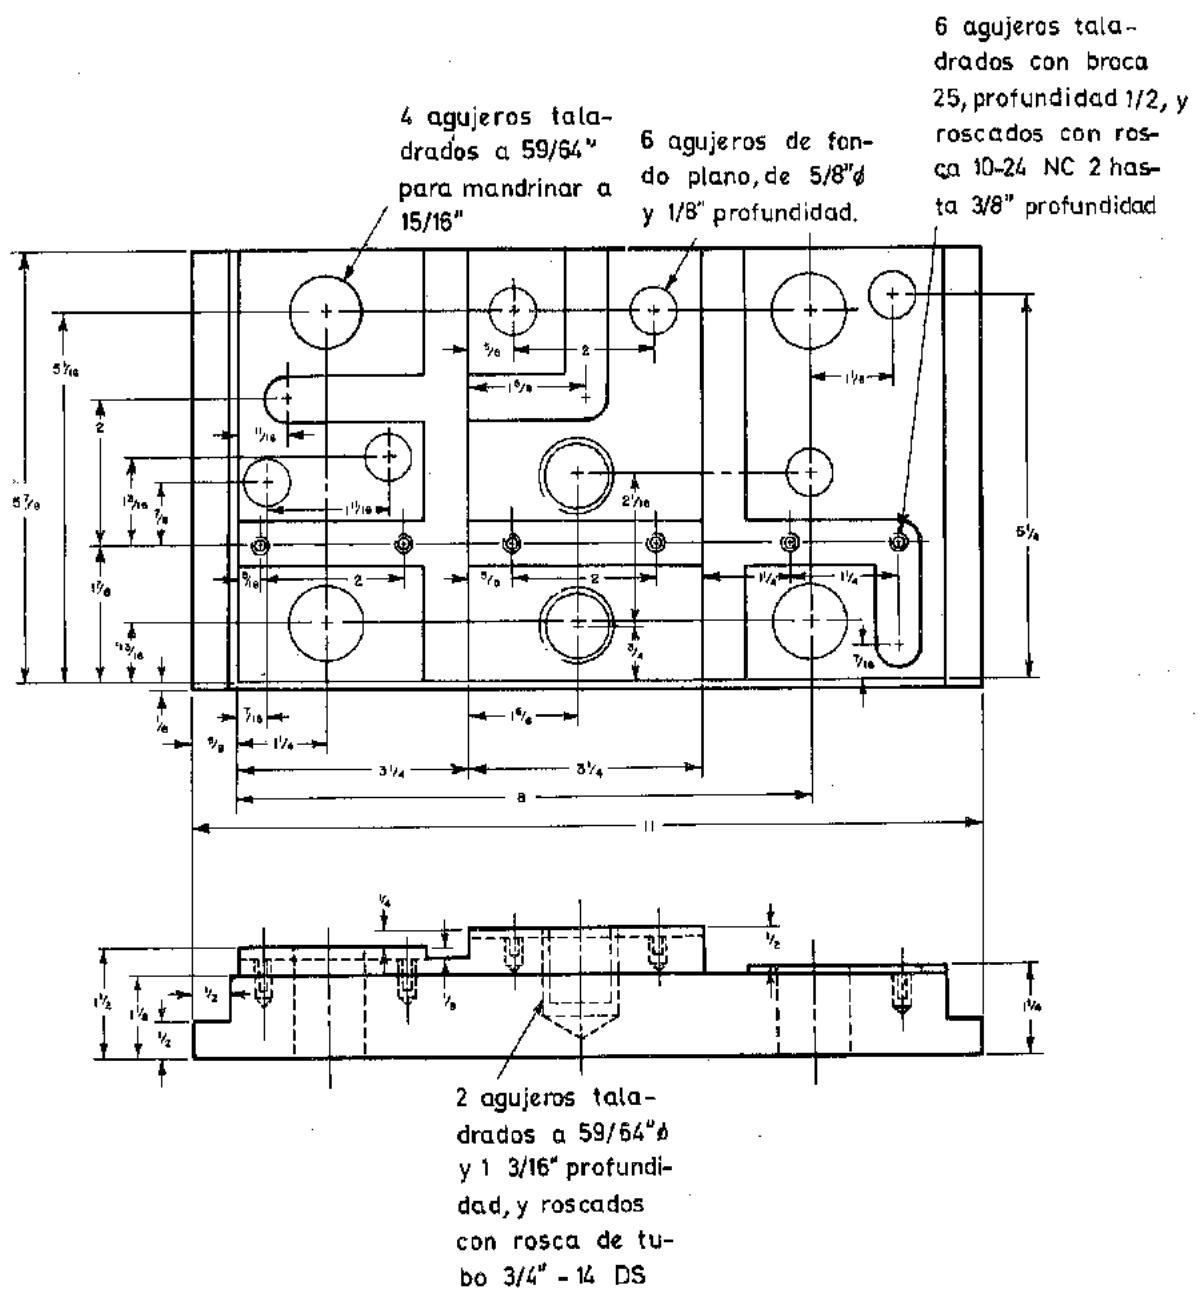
Dibujo de un banco de pruebas dimensionado en pulgadas del modo tradicional (Cincinnati Milling Machine Co.)
